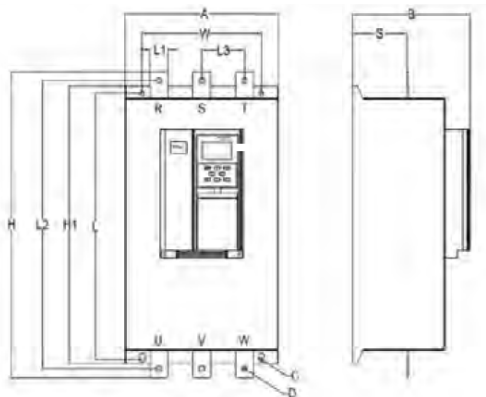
Габаритные и установочные размеры корпуса и медных шин для кода RR2, RR3.
